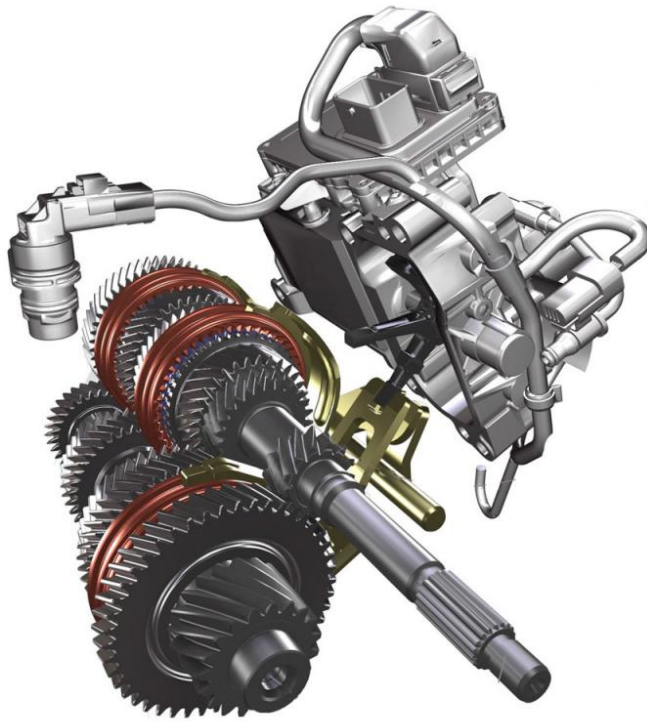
Конструкція роботизованої механічної коробки передач
